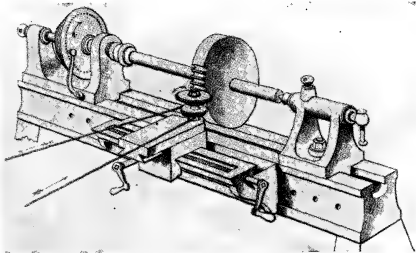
Принципиальная схема зуборезно-фрезерного станка. 1841 г. По Нэсмиту.
